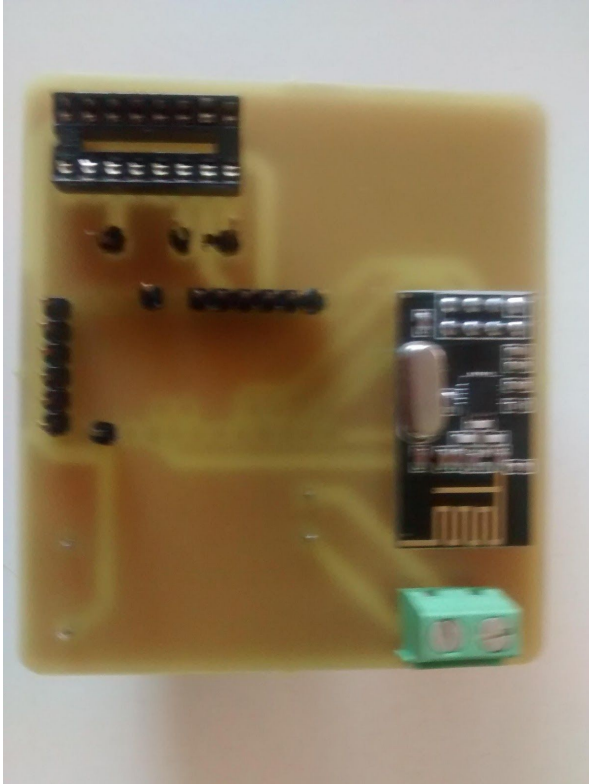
y 3.15: Placa de la segunda PCB soldado superior e inferior
